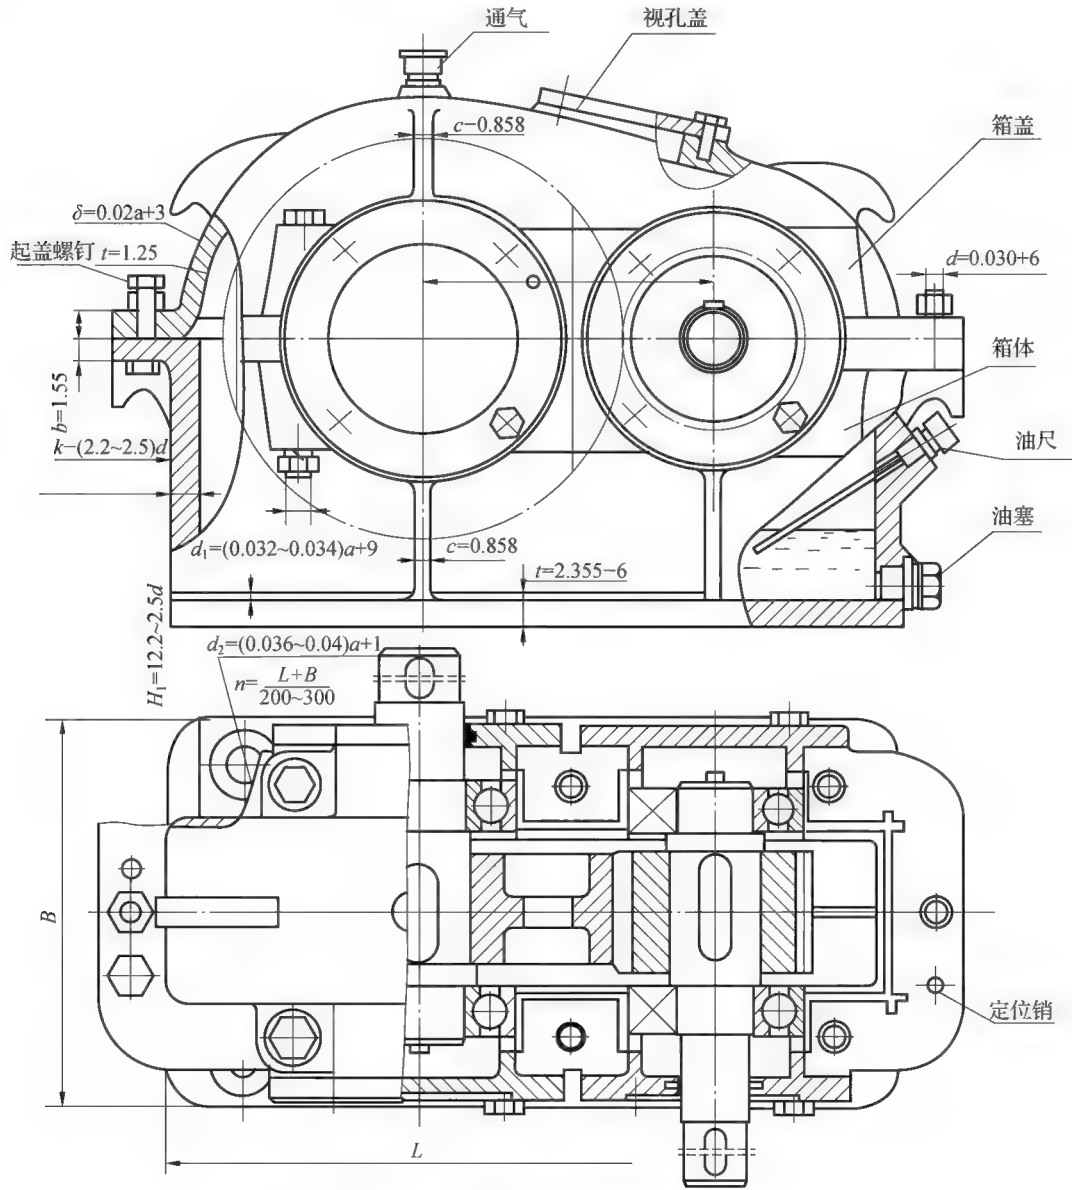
单级圆柱齿轮减速器结构(单位: mm)
